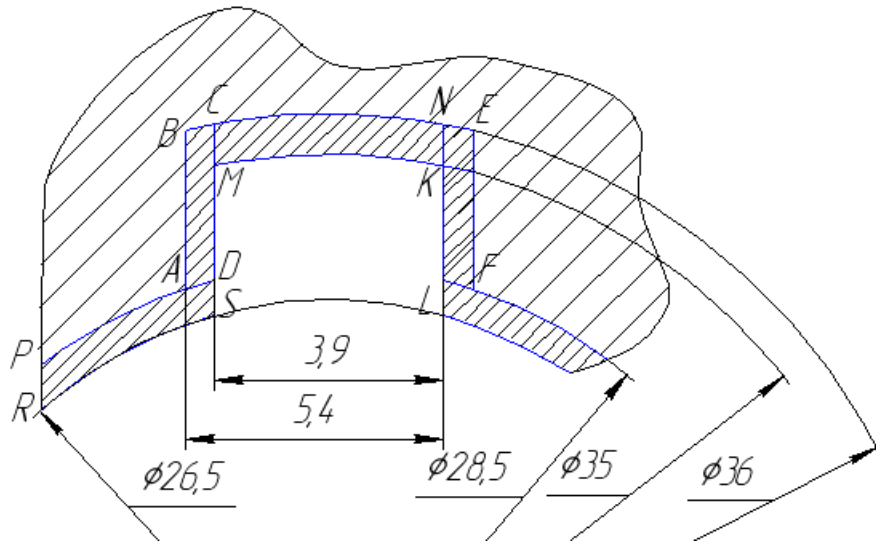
Схема розміщення та величина припусків на робочі поверхні шліців втулки маточини
